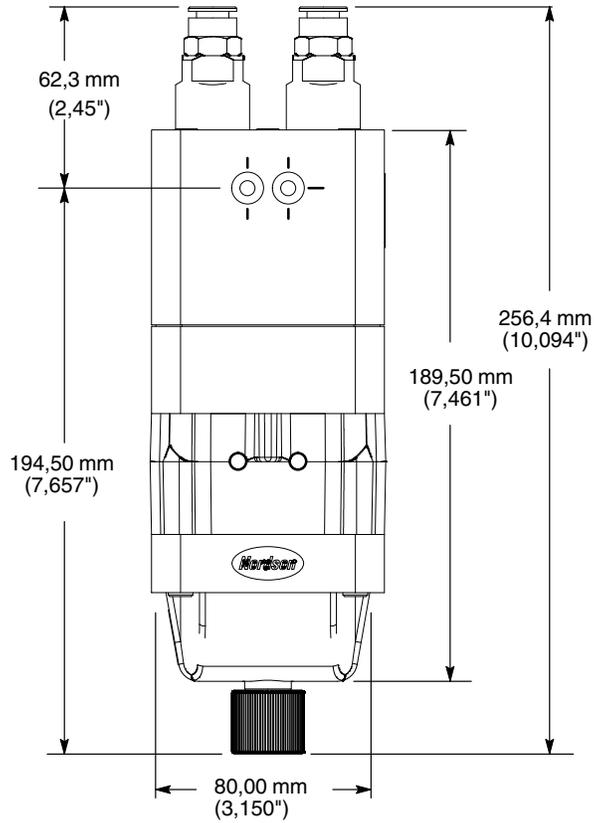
Dimensions de la pompe HDLV Prodigy standard
